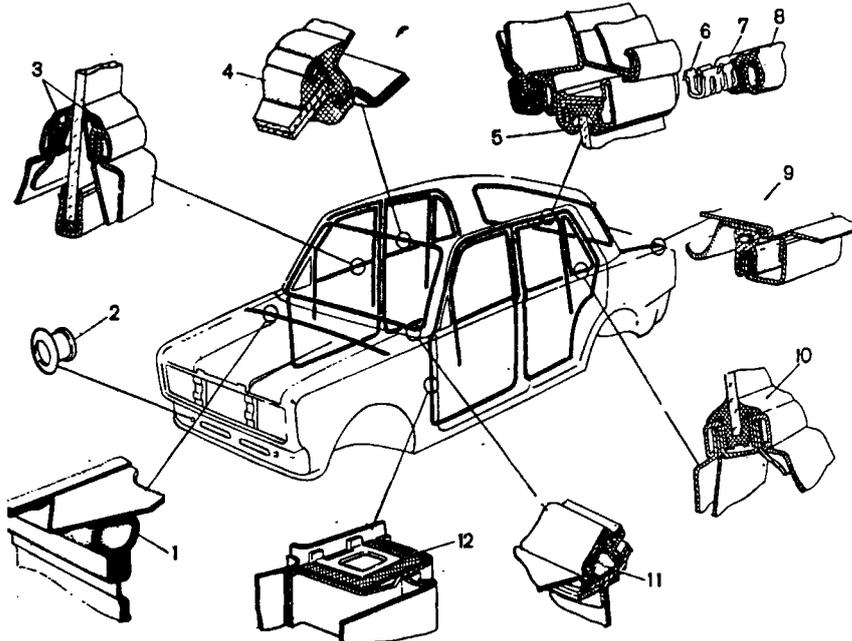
Резиновые уплотнители: 1 - капота; 2 - соединителя бампера; 3 - нижний уплотнитель стекла двери; 4 - ветрового и заднего стекла; 5 - опускного стекла; 6 - каркаса уплотнителя; 7 - кант уплотнителя; 8 - проема дверей; 9 - крышки багажника; 10 - неподвижного для стекла двери; 11 - рамы ветрового окна; 12 - передней стойки
